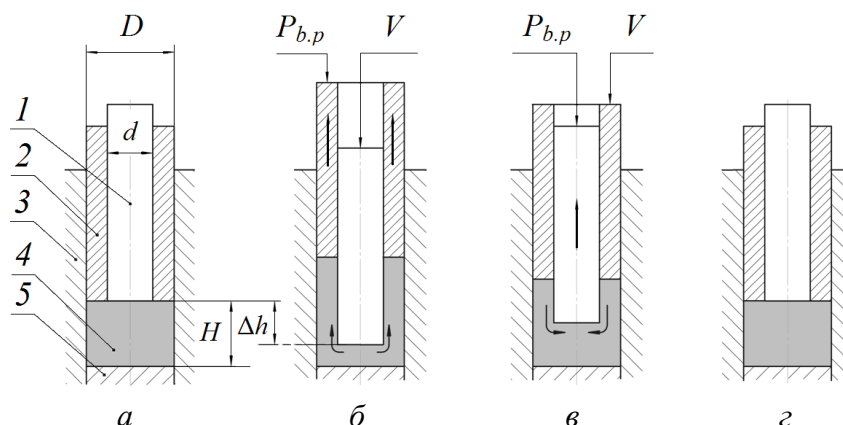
Расчетная схема процесса РЗП: *а* – исходное положение заготовки, *б* – закрытая прошивка, *в* – реверсирование, *г* – конец цикла; 1, 2 – соответственно внутренний и внешний пуансоны, 3 – штамп, 4 – заготовка, 5 – выталкиватель
